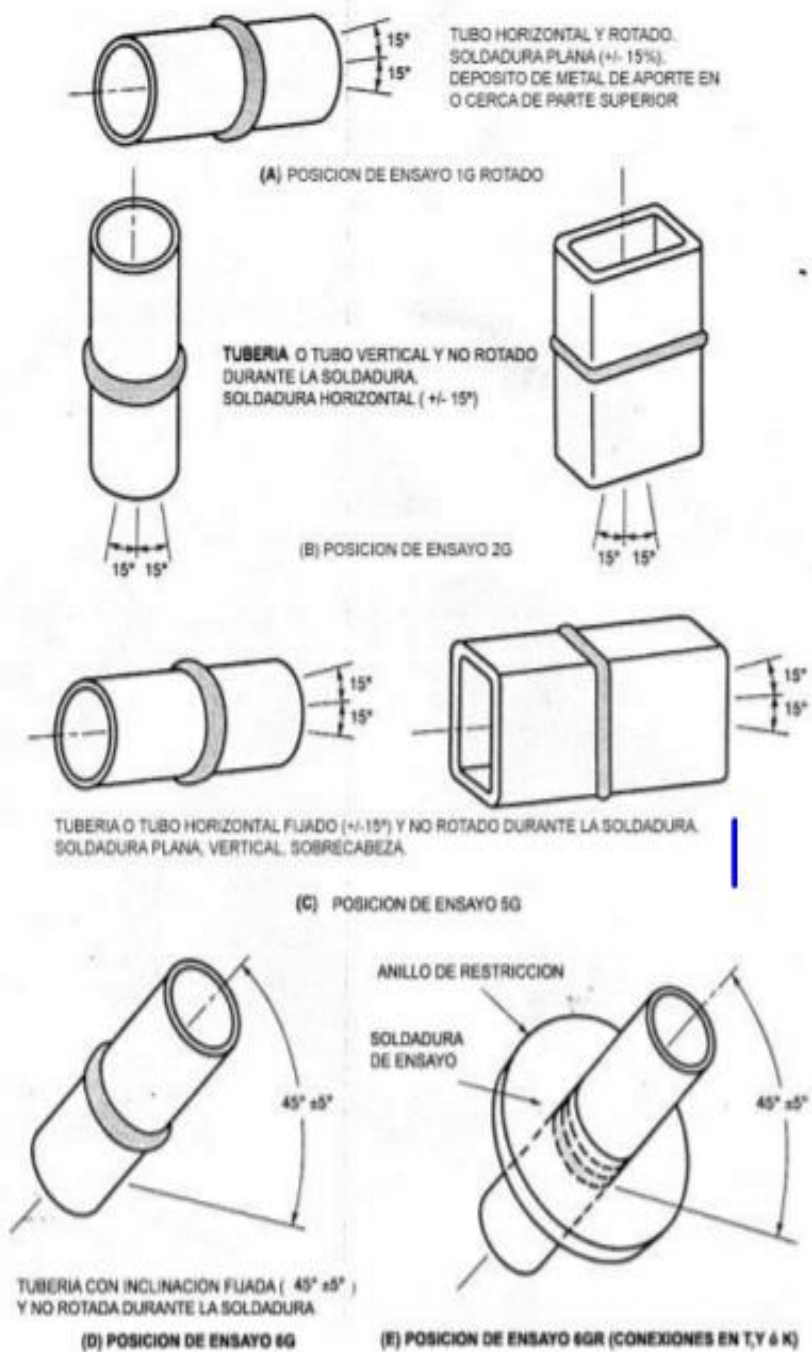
Posiciones de Tubo o Entubado de Ensayo para Soldaduras de Ranuras (ver 4.2.4)
